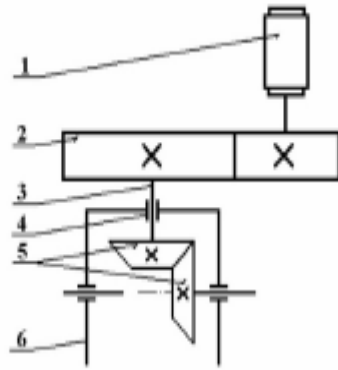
Кинематическая схема привода с коническим зубчатым редуктором:
